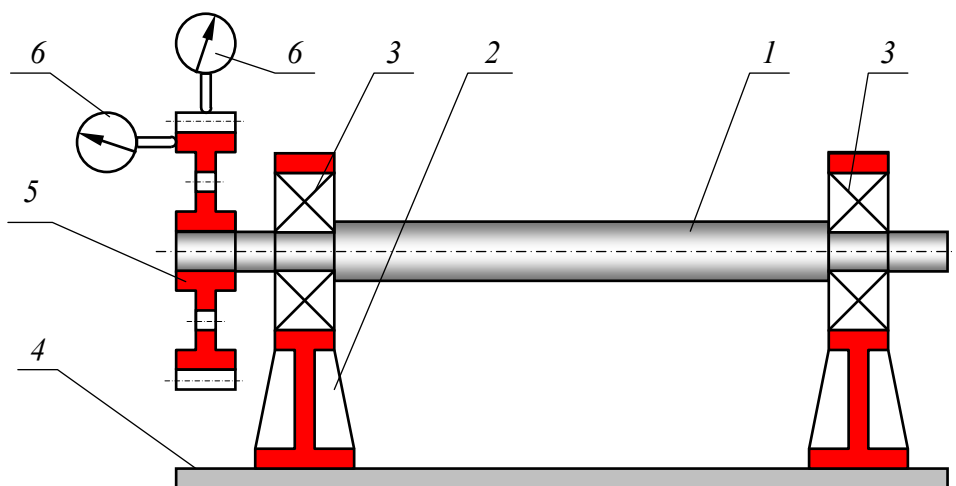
Схема стенда для проверки радиального и торцового биения шестерен:
